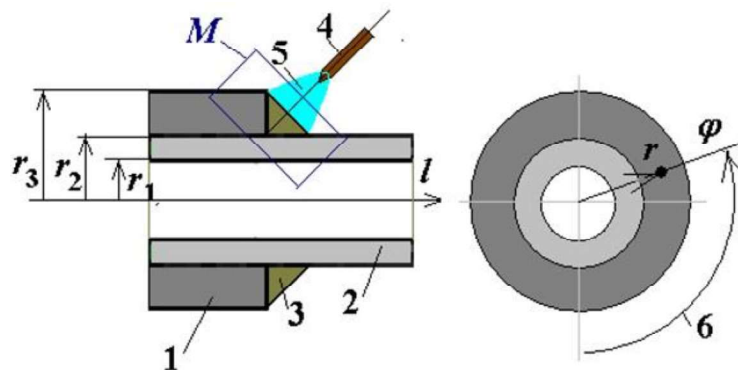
Конструкция свариваемого стыка в положении выполнения сварки:
